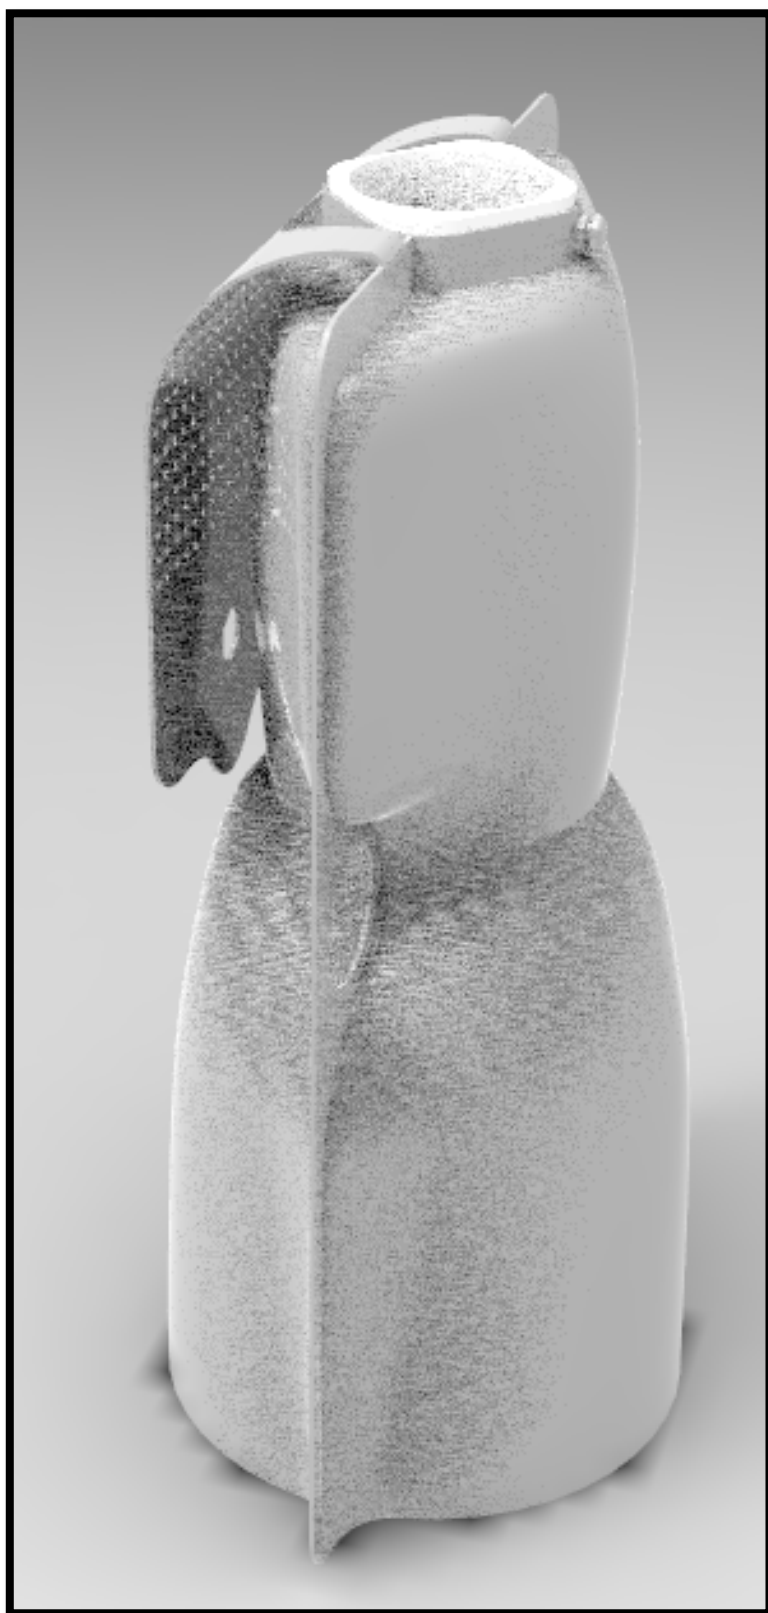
Vista en detalle del accesorio donde se encastra el pre-filtro para su uso.
